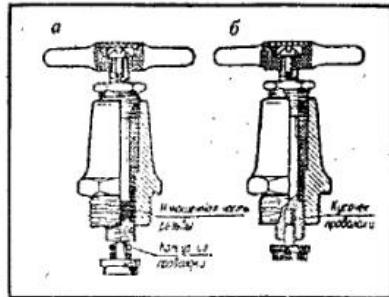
Временный ремонт изношенной резьбы штока вентильной головки
